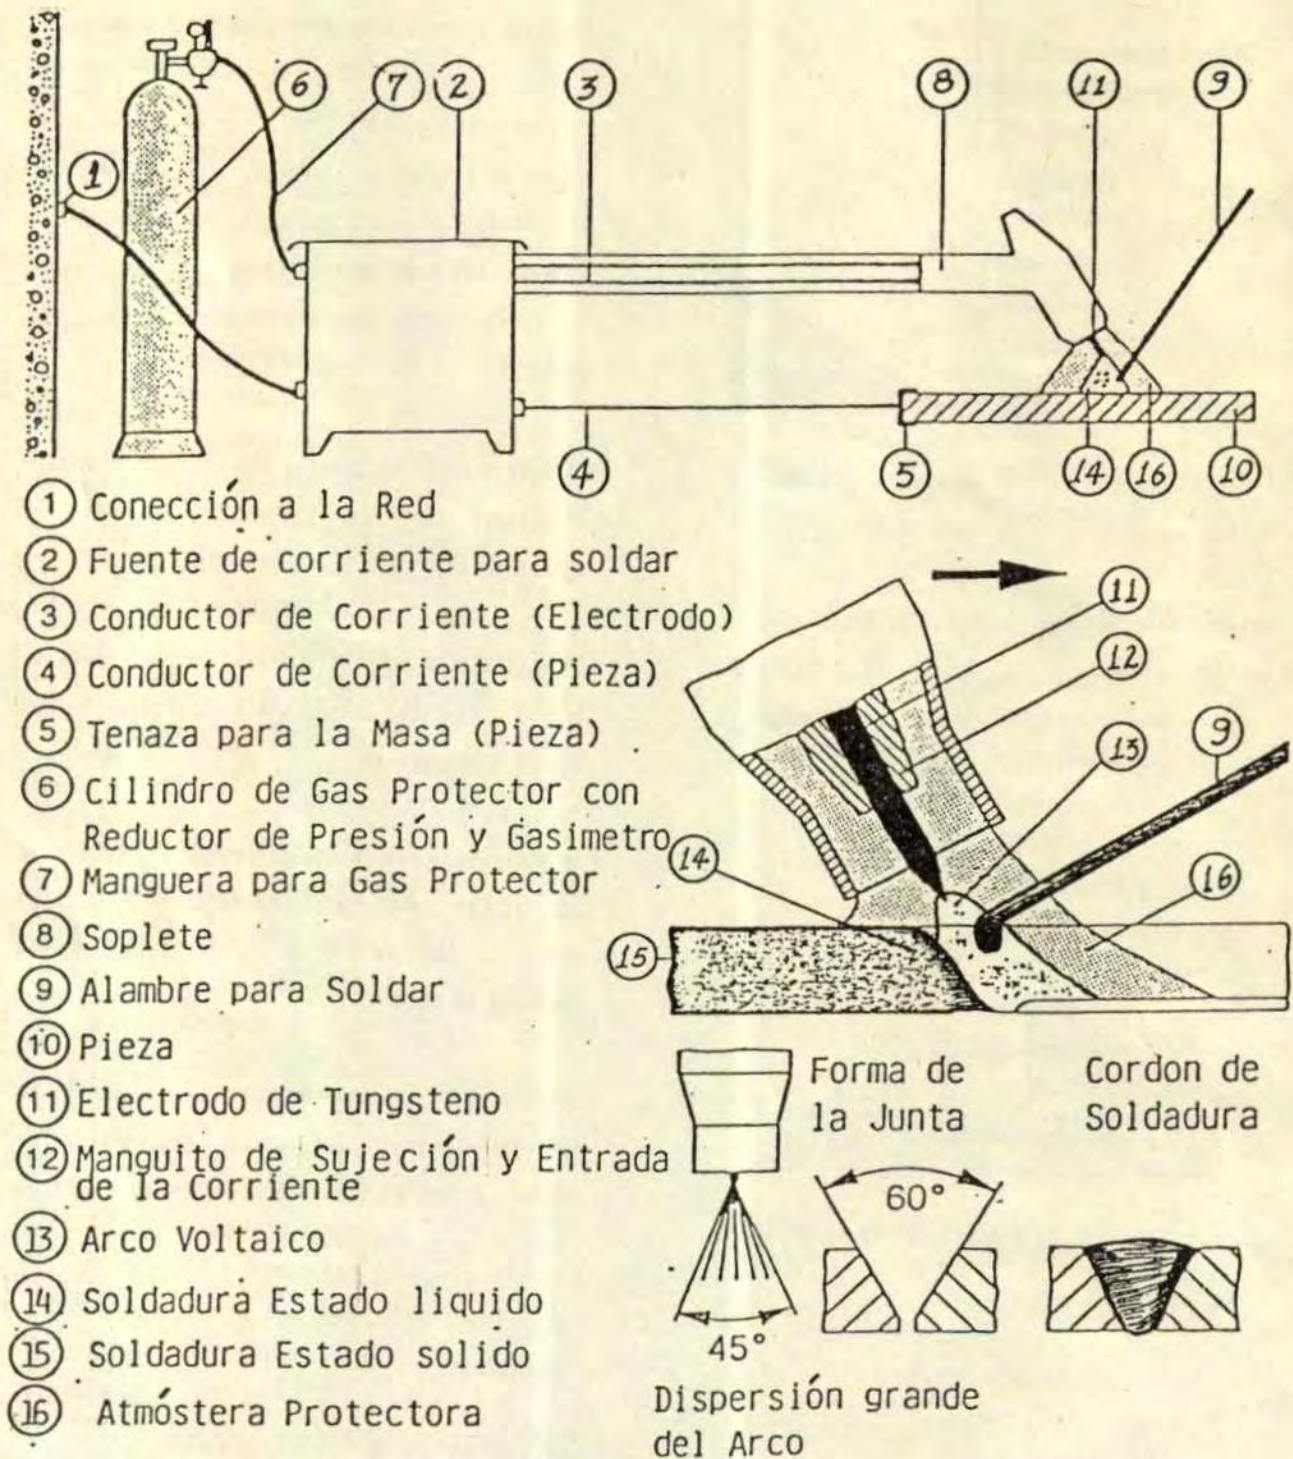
Representación esquemática del equipo para soldadura TIG.
